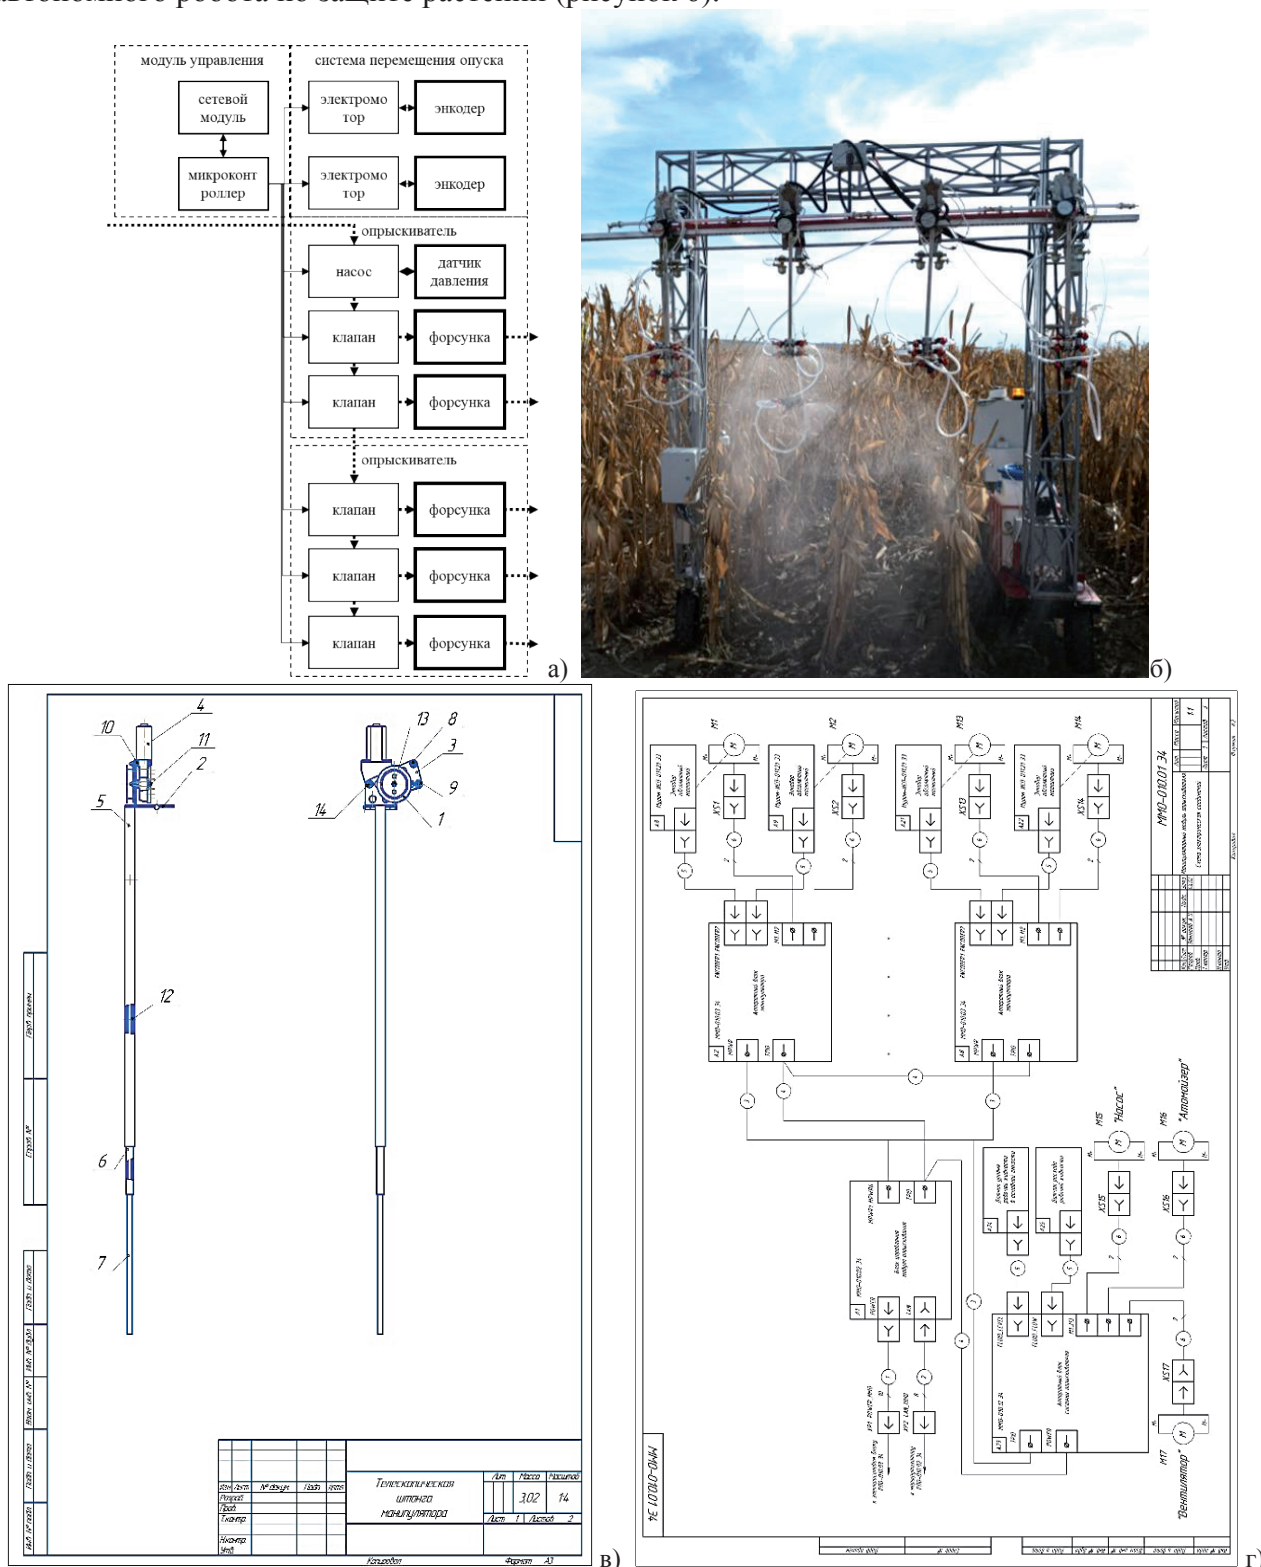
Схема (а), внешний вид (б) и чертежи (в, г) манипулятора опрыскивателя
